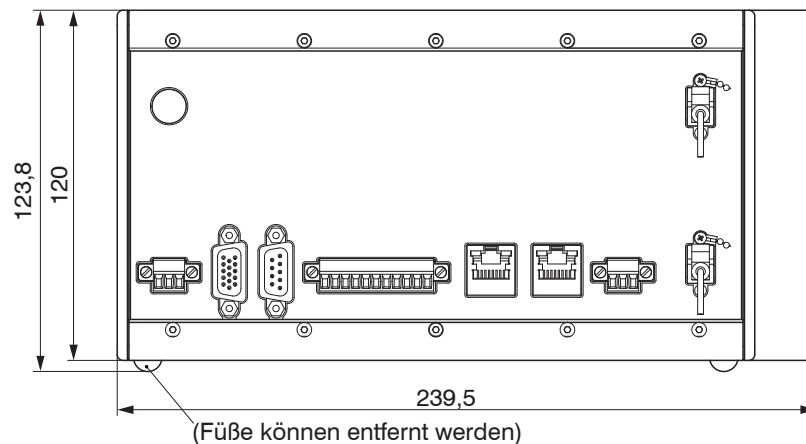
Maßzeichnung Frontansicht des Controllers IFC2422/2466, Abmessungen in mm
